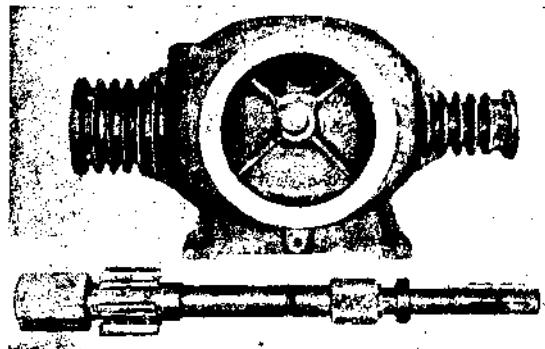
Двойной инструмент Hutto для цилиндра ступенчатого компрессора.
